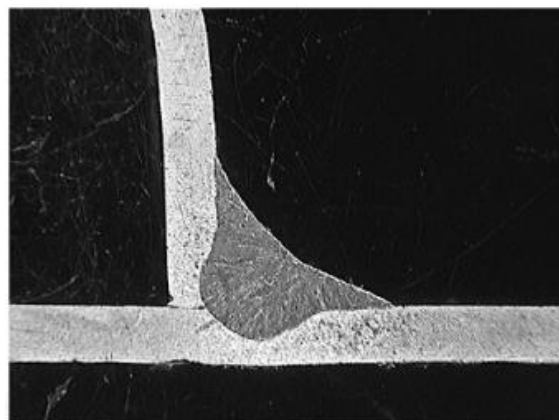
Soldadura ideal [Fonte: Documentação interna da Empresa].
